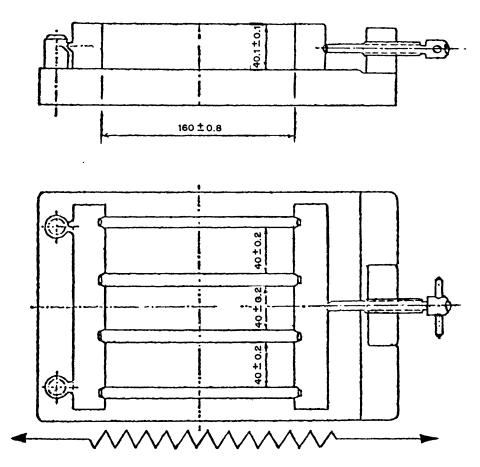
Ejemplo de molde. Dimensiones en mm.
